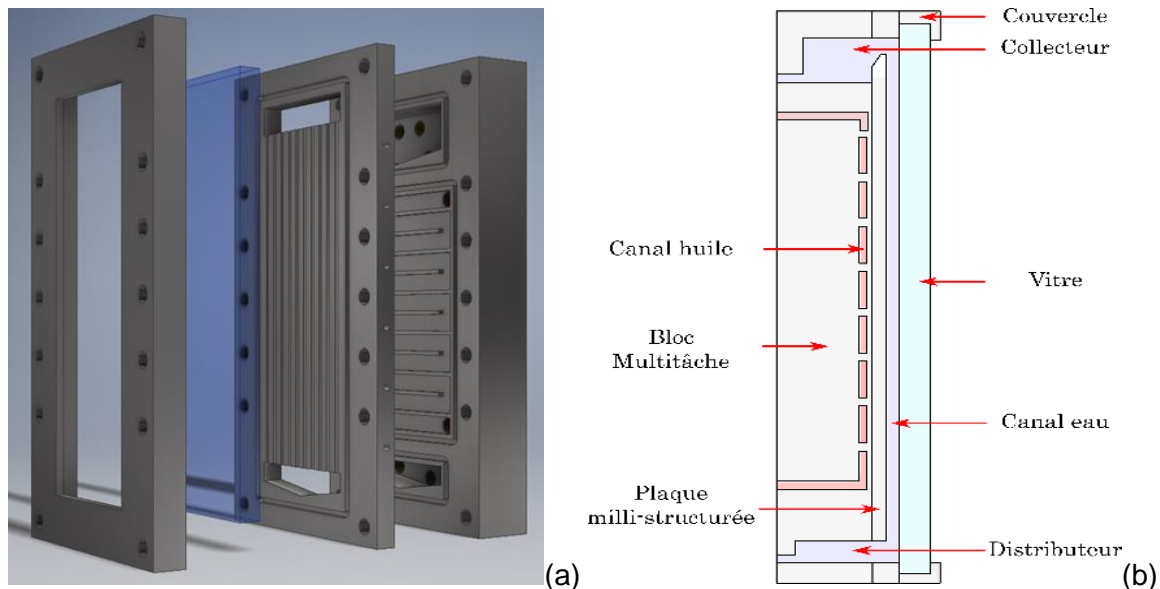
Vue explosée (a) et vue en coupe (b) de la structure du vaporiseur
